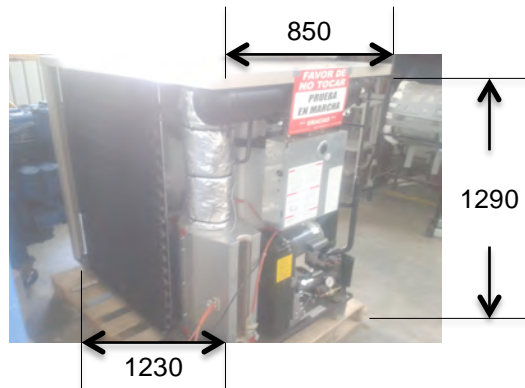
Dimensiones expresadas sobre la máquina (en milímetros).
